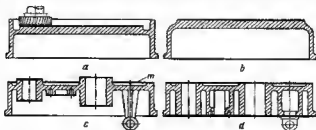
Mecanizado de piezas tipo armazón de una pasada
